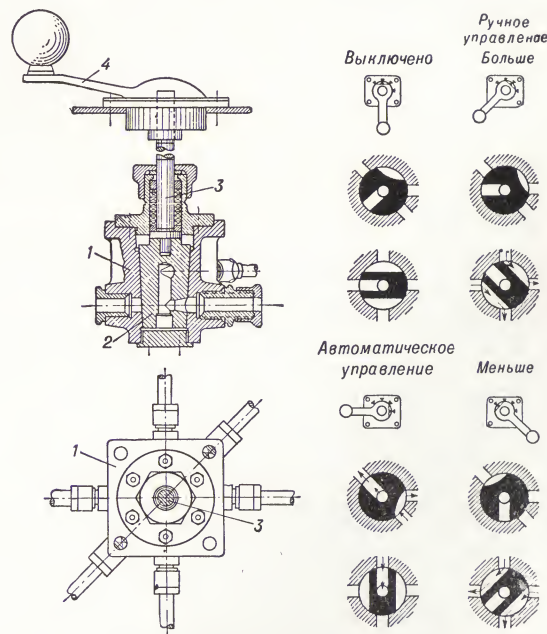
Кран-переключатель для переключения двух потоков на четыре направления: 1 — корпус; 2 — пробка; 3 — вал; 4 — ручка.
